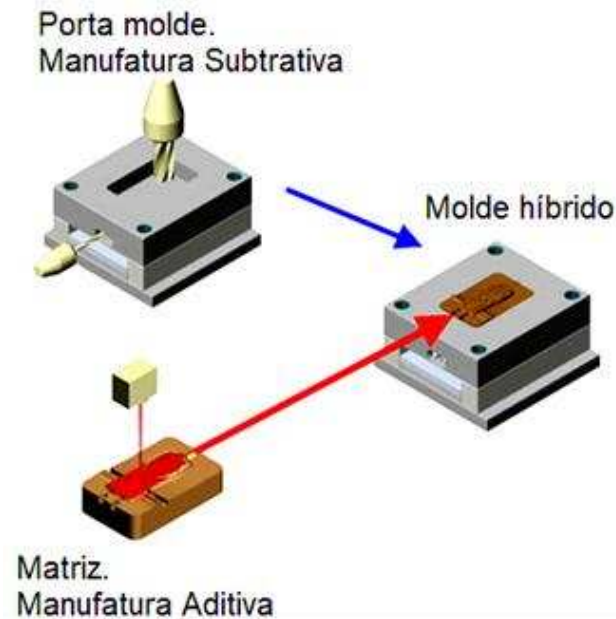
Conceito de fabricação de um molde mecânico do tipo híbrido.
